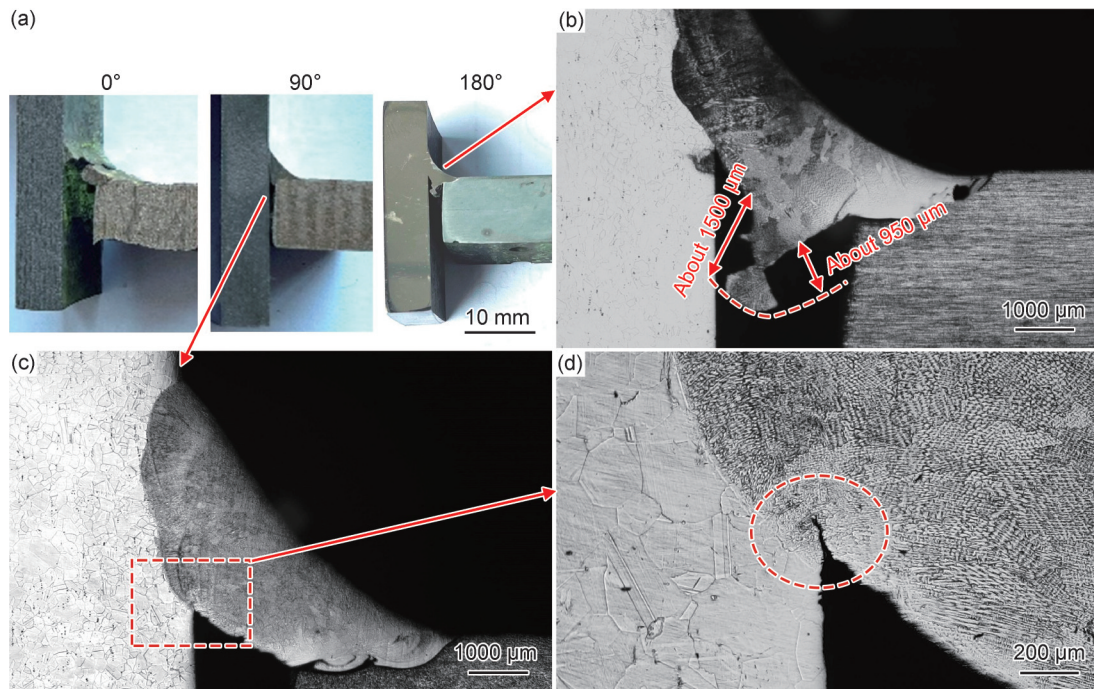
筒体 2 与栅板焊接接头不同位置的宏、微观形貌
